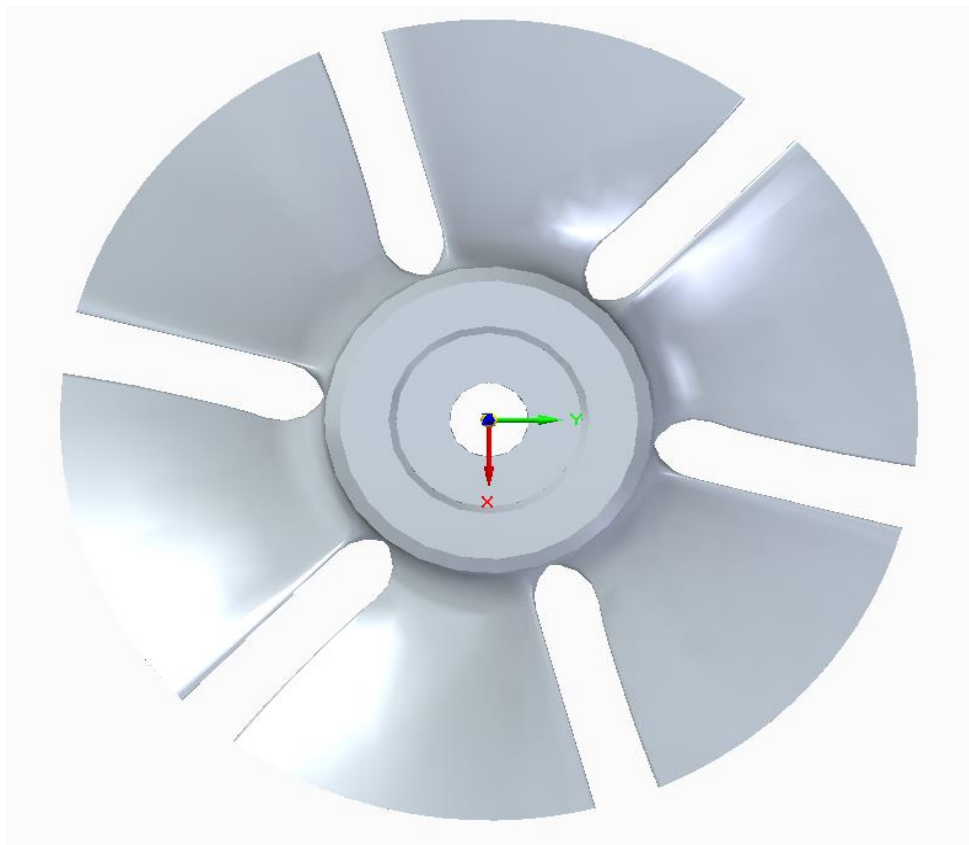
Vista de planta del rodete acabado. (Elaboración propia)
